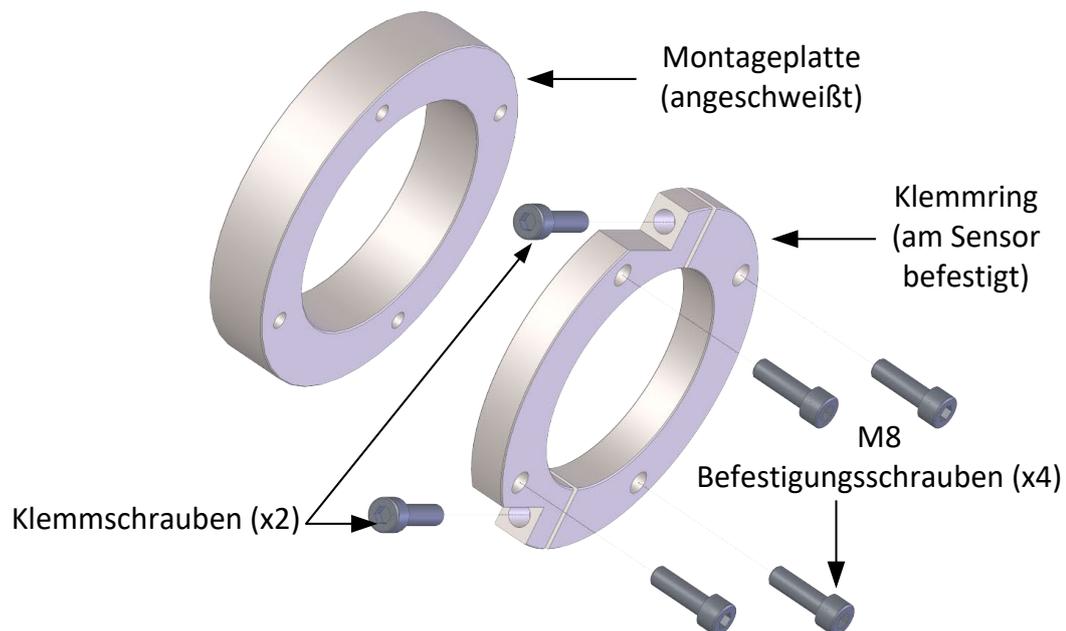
Hydro-Mix HT – Befestigungskomponenten
